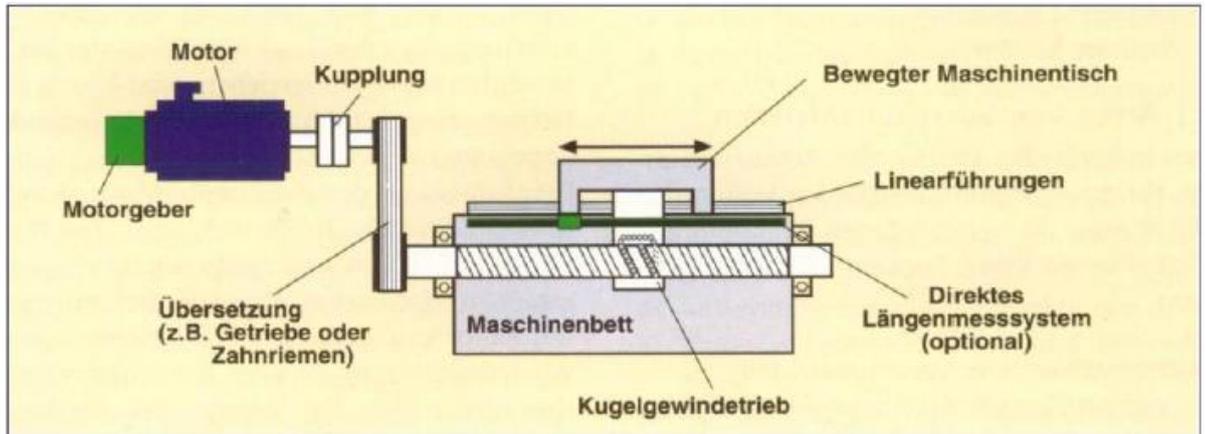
Elektromechanischer Vorschubantrieb einer Werkzeugmaschine
